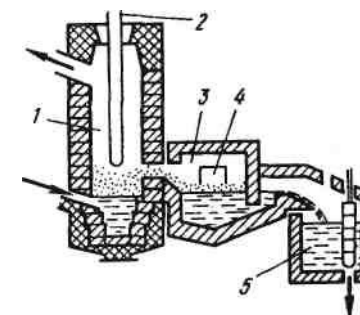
Схема установки для непрерывного рафинирования конструкции IRSID
